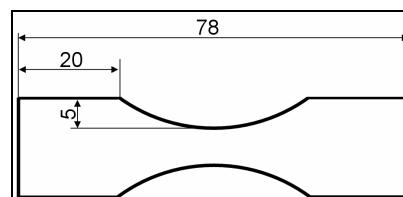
Dimension des éprouvettes (épaisseur 2 mm).
